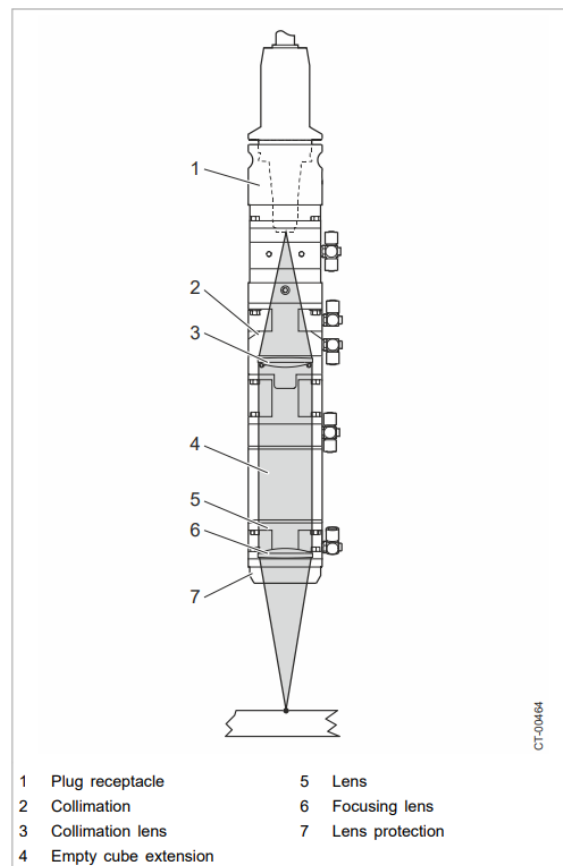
Configuração básica do dispositivo de focagem ótica de soldadura(Trumpf, 2020).
